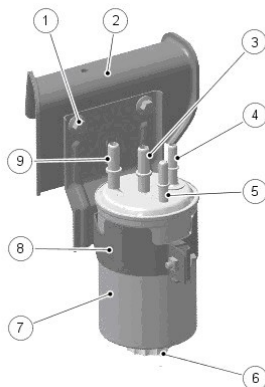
Топливный фильтр дизельного двигателя 2.7 TD V6
